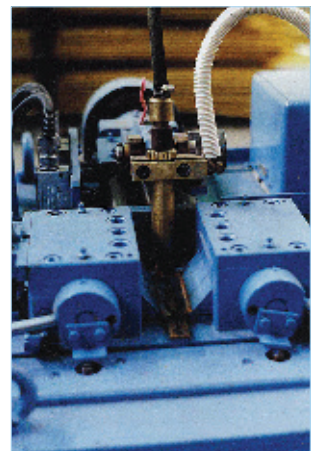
Обрезка переднего и заднего концов рулона, стыковка и поперечная сварка концов
